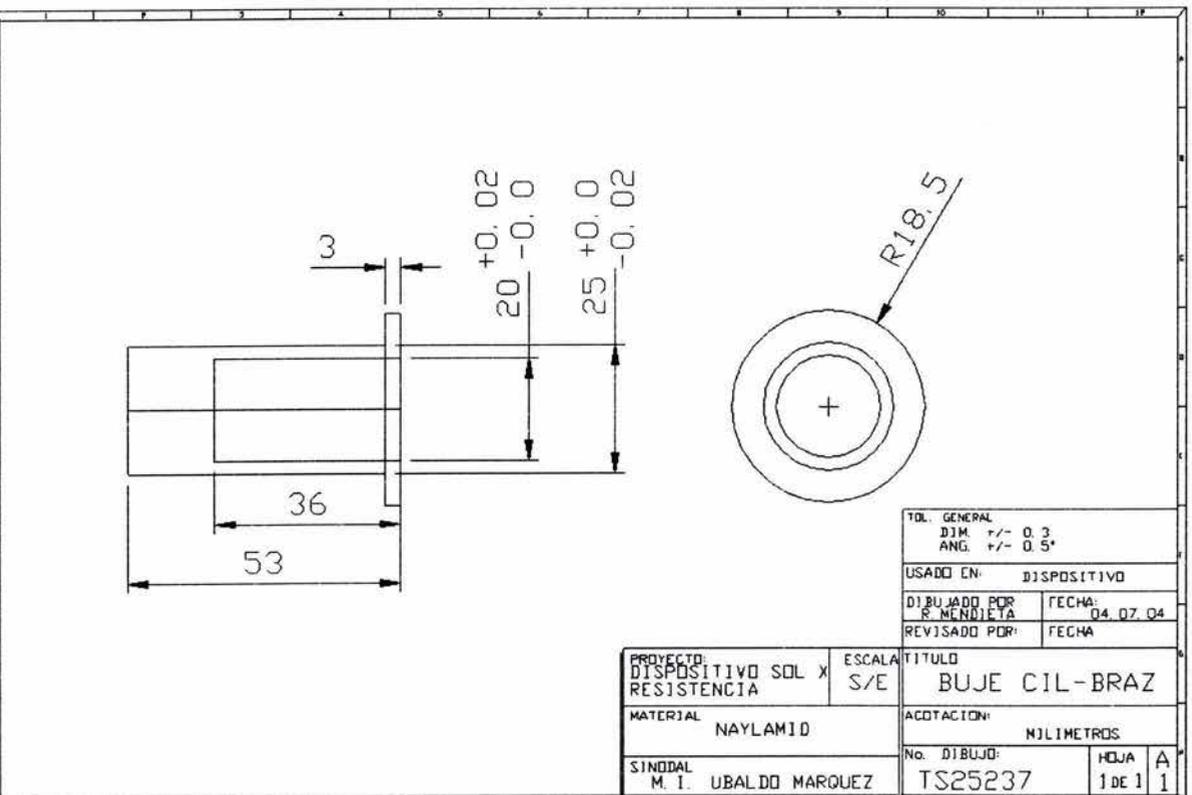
Bujes de aislamiento entre el brazo móvil y el cilindro de soldadura.
